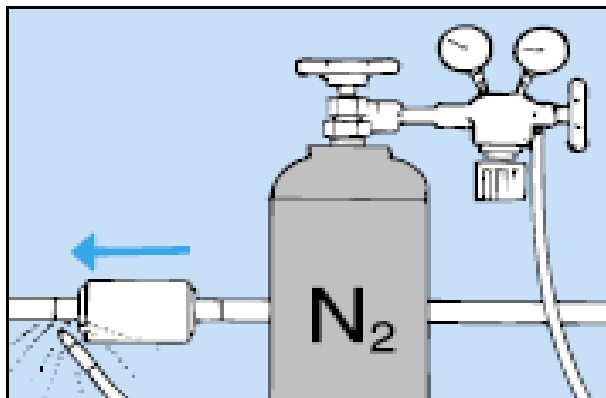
soldadura con gas protector nitrógeno
